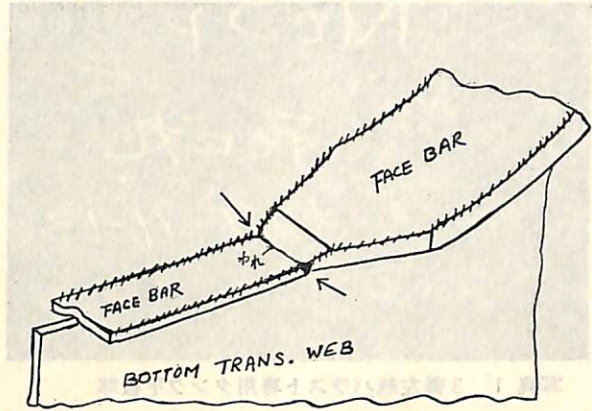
フェイスバーの角の部分に沿って発錆矢印のところがノッチ状に腐蝕し溶接部が割れた
